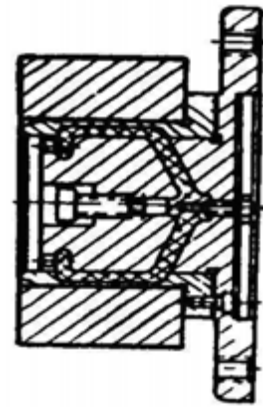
Установка заготовок на розтискній оправці з гідропластом
